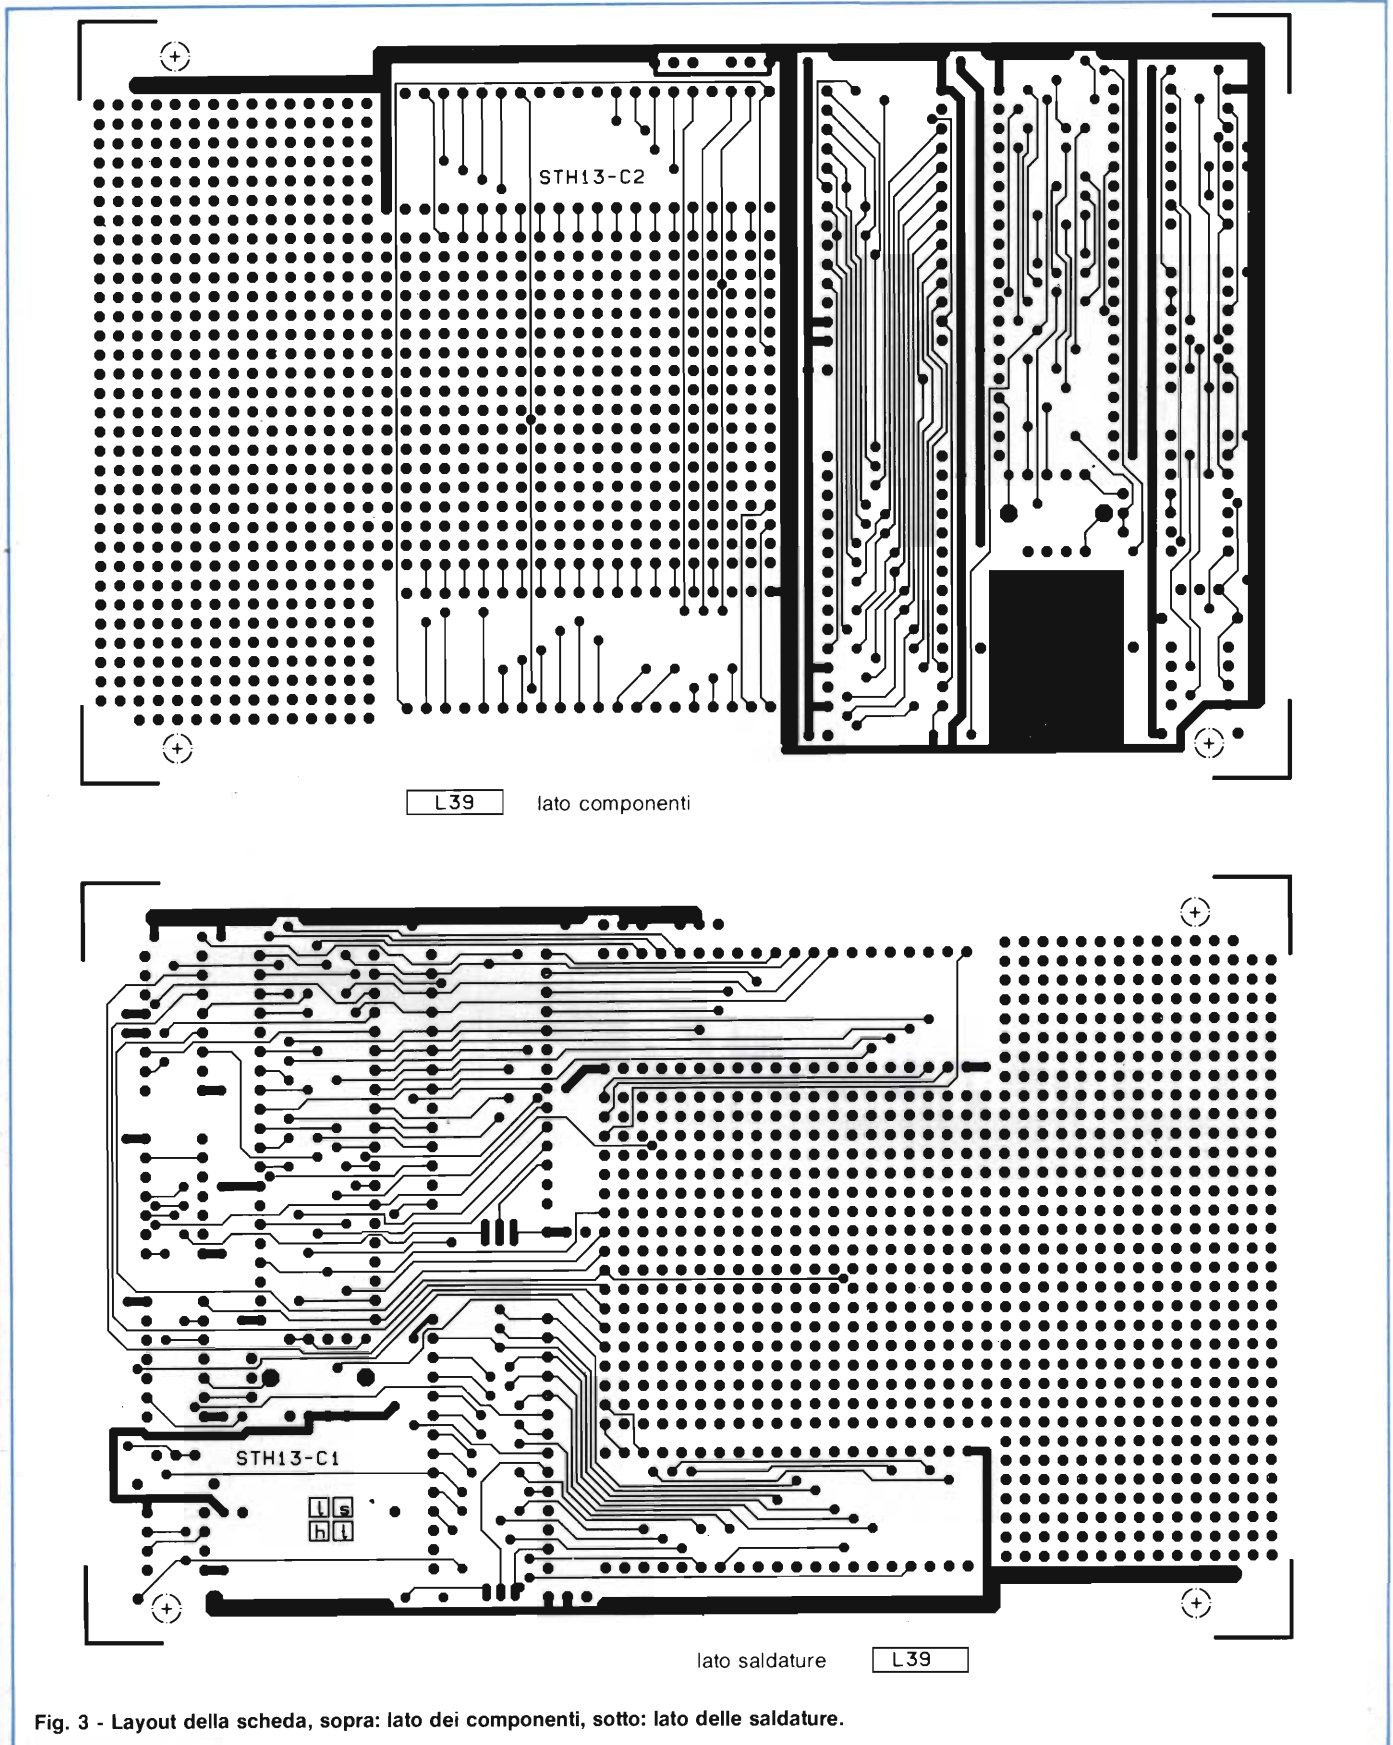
Layout della scheda, sopra: lato dei componenti, sotto: lato delle saldature.
